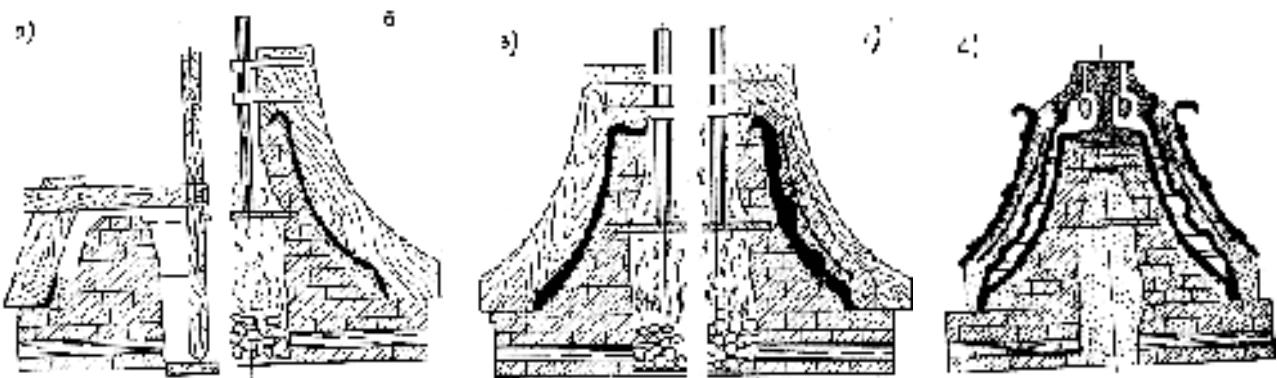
Схема изготовления формы колокола: а - изготовление основы болвана; б - заточка болвана; в - заточка рубашки; г - готовая форма
